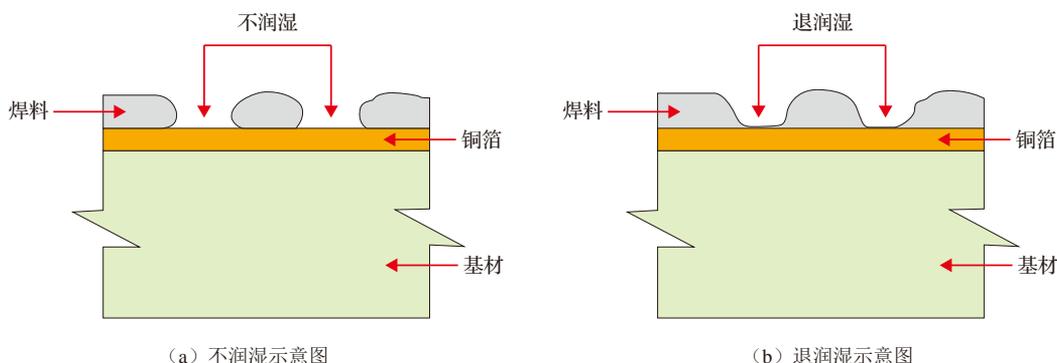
PCB 焊盘表面喷锡焊料涂覆层不润湿与退润湿示意图
